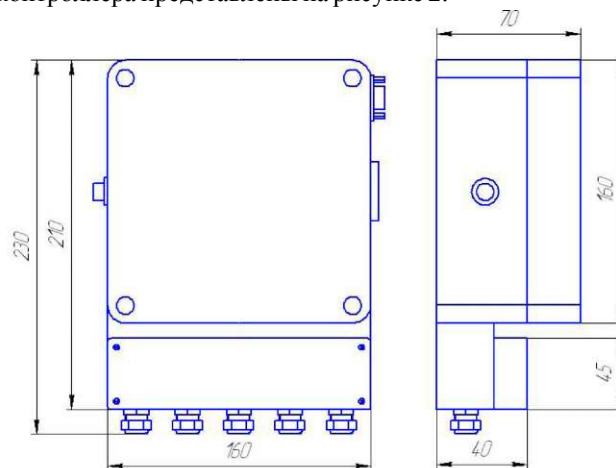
Габаритные размеры контроллера СГМ ЭРИС-120
